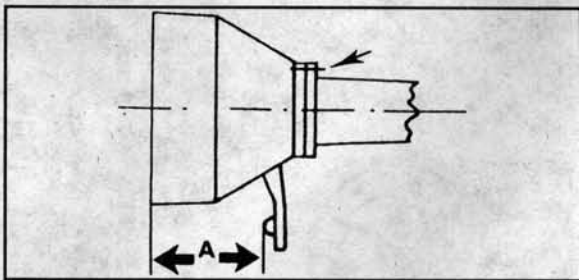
Регулировка сцепления, сопряженного с механической КПП (сцепление с неподвижным выжимным подшипником)
